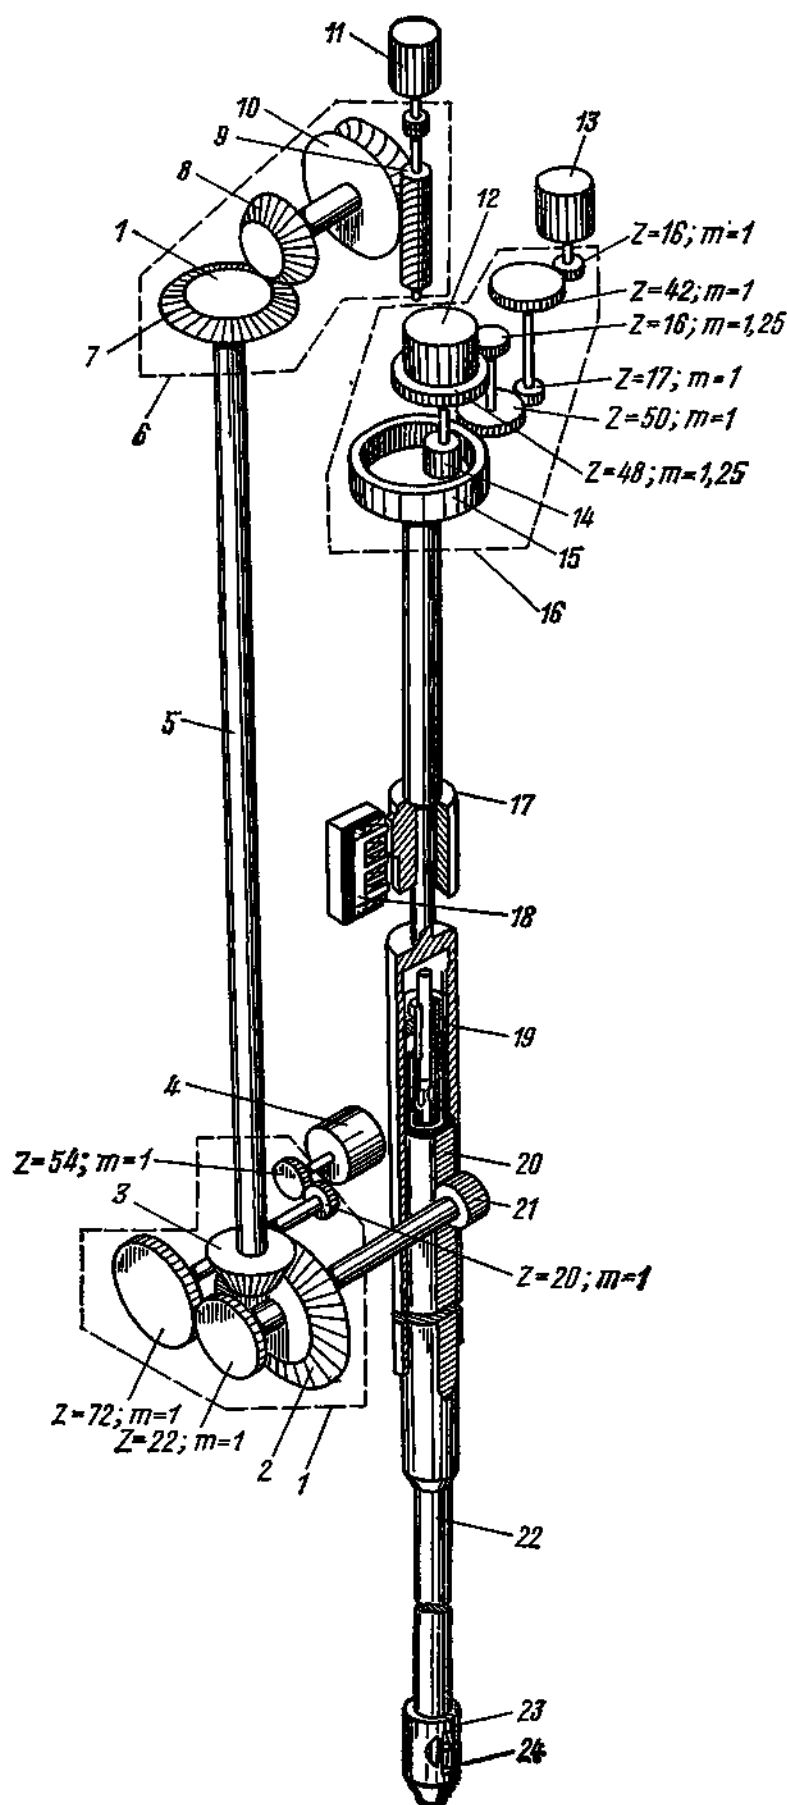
Общий вид исполнительного механизма СУЗ реактора БН-600:
